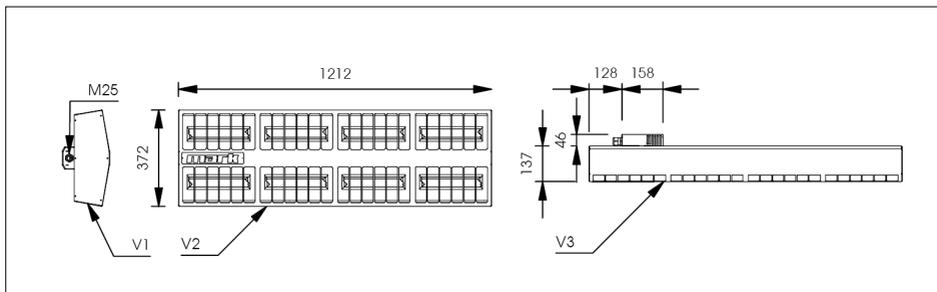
Dimensions du INFRA ER 6400. (V1 : Vue latérale gauche, V2 : Vue de dessous, V3 : Vue de face)
